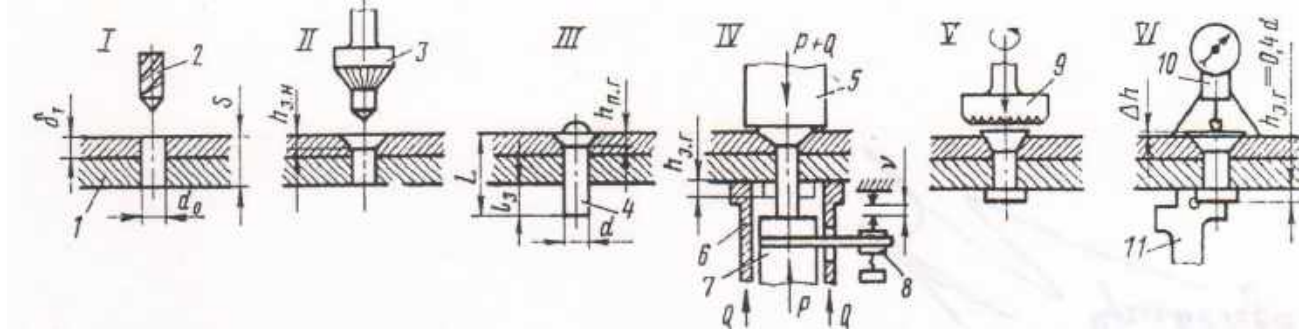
Елементи клепання: 1 – пакет, що склепується; 2 – свердло; 3 – зенкер; 4 – заклепка заглиблена з компенсатором (ЗУК); 5 – верхній пуансон; 6 – притискач; 7 – нижній пуансон; 8 – система мікро-вимикачів; 9 – торцева фреза; 10 – індикатор з підставкою; 11 – шаблон
